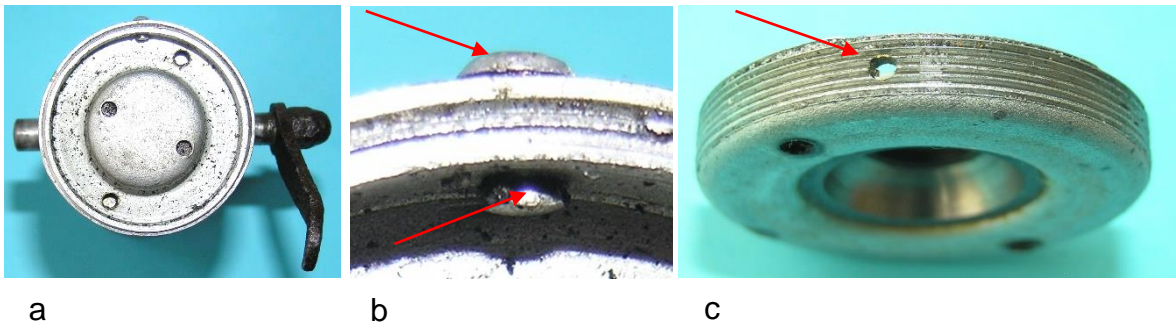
Befestigung des Bodens im Lagerhalstopf: a) Bodenansicht des Generators, b) Sicherungsniets, c) Nietbohrung im Bodengewinde
